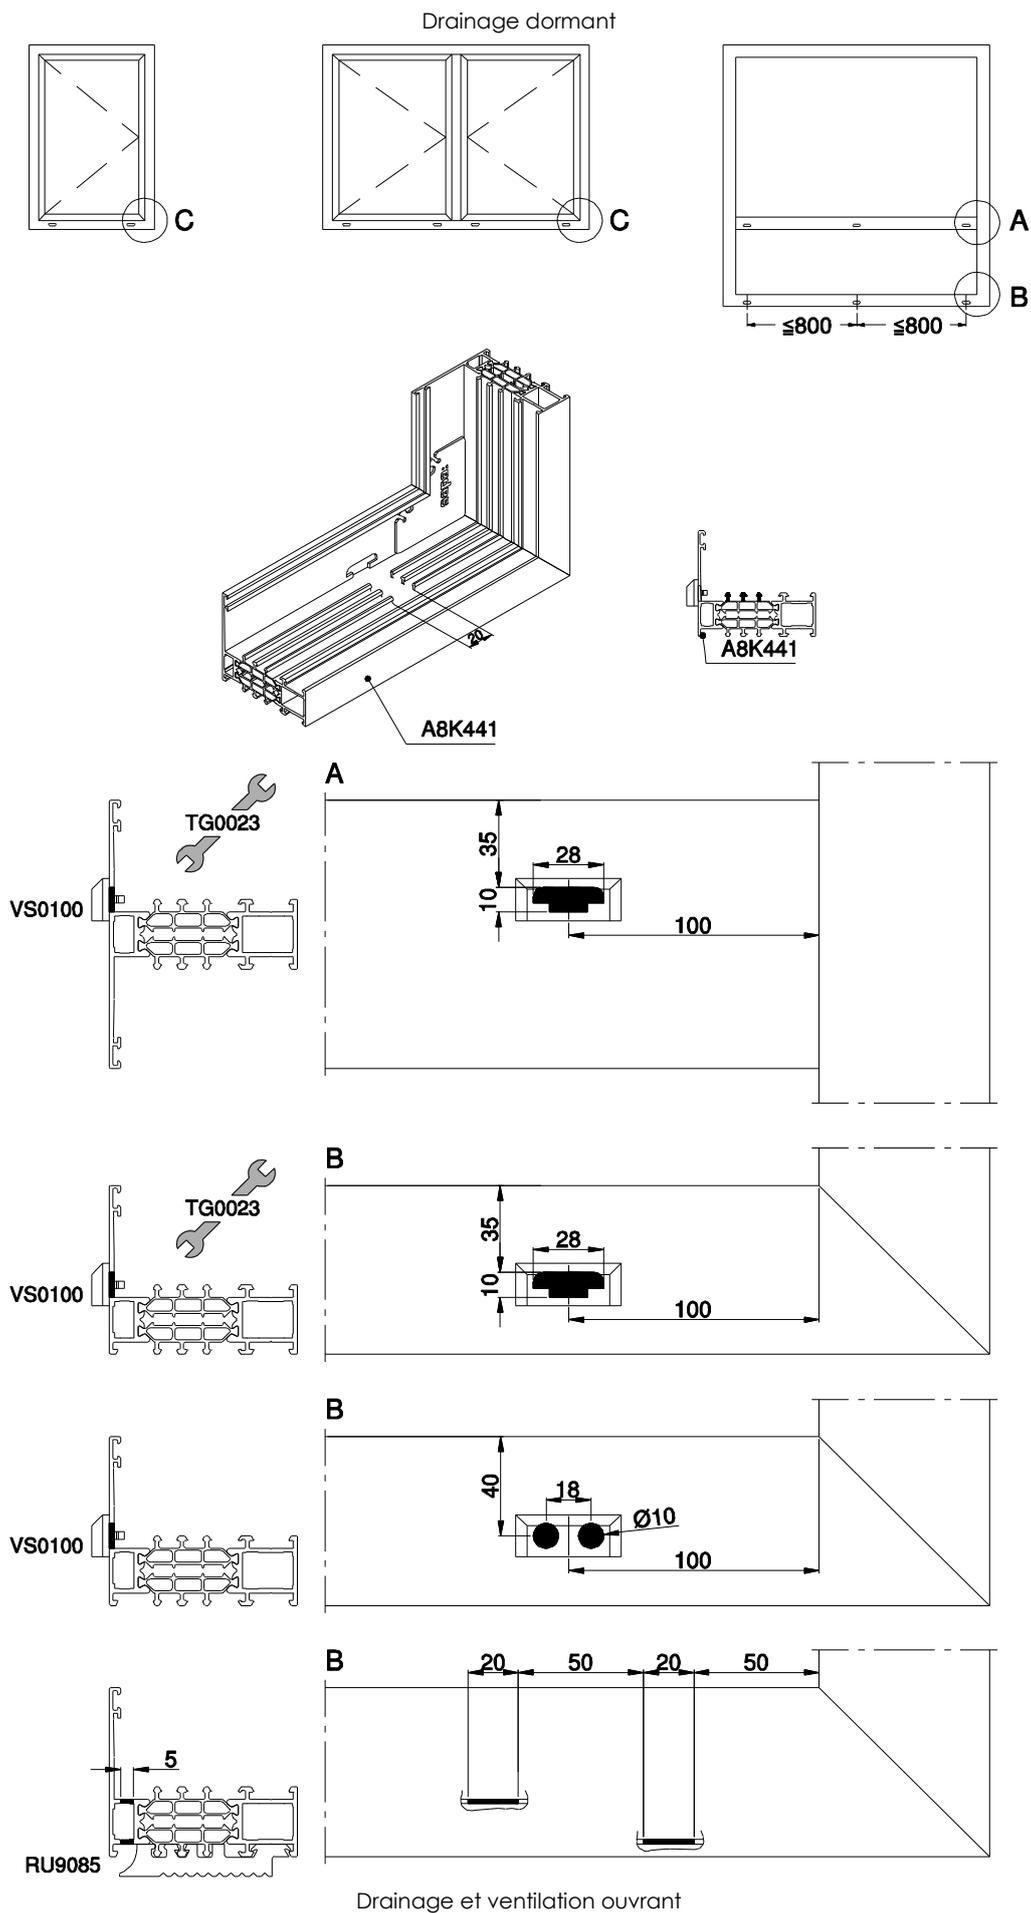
(suite) – Drainage de la feuillure et de la battée et ventilation
